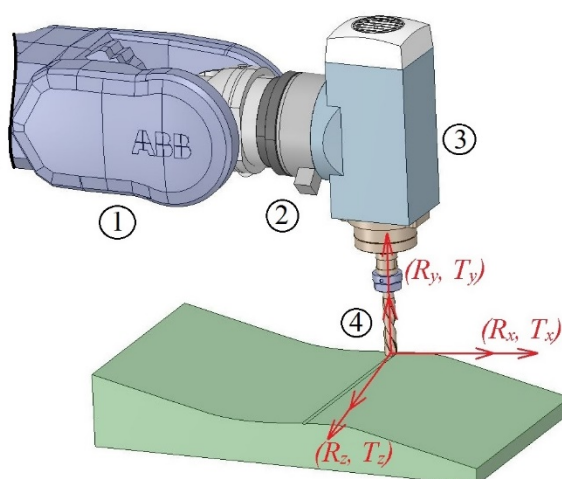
3D – модель зоны контакта инструмента и обрабатываемой поверхности
